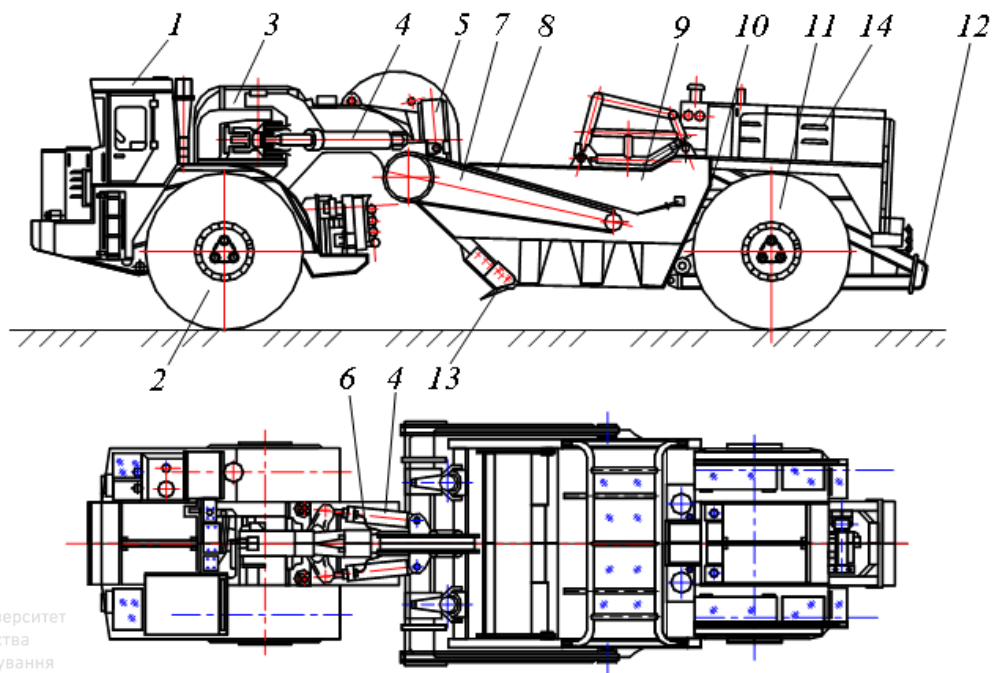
Конструктивна схема самохідного двомоторного скрепера:
